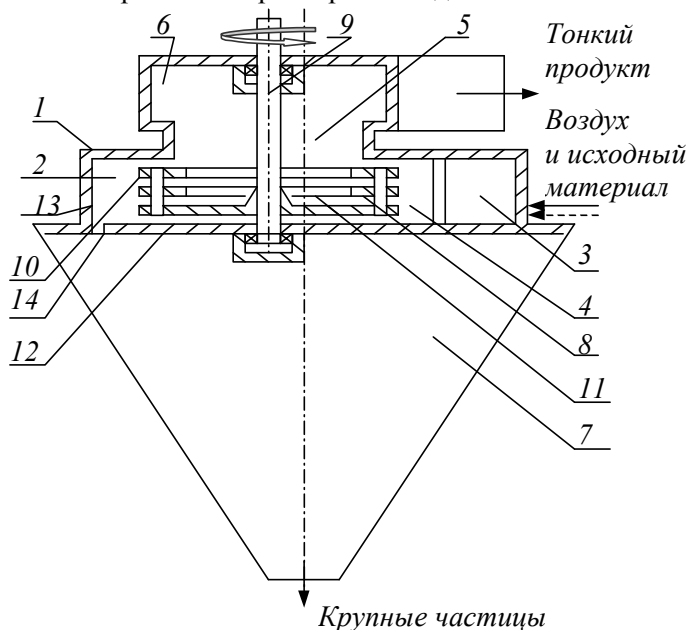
Центробежный классификатор: 1 – корпус; 2 – спиральная камера; 3, 4 – патрубки подачи потоков воздуха и исходной смеси; 5 – патрубок для вывода воздуха с мелкими фракциями; 6 – улитка выходная; 7 – бункер грубого продукта; 8 – пакет дисков; 9 – вал; 10 – радиально-тангенциальные каналы; 11 – аксиальный канал; 12 – днище камеры; 13 – боковая стенка камеры; 14 – концентрическая щель для вывода крупных фракций.
